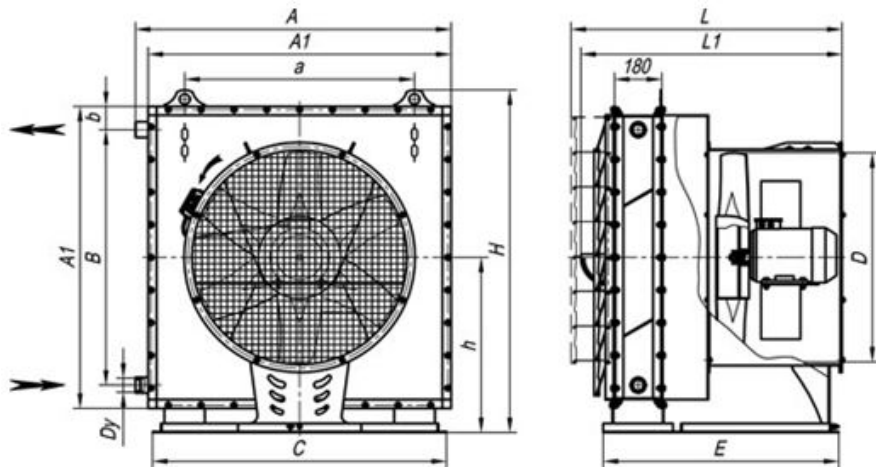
Габаритные размеры агрегата воздушно-отопительного АО2 на базе калориферов типа КСк.
